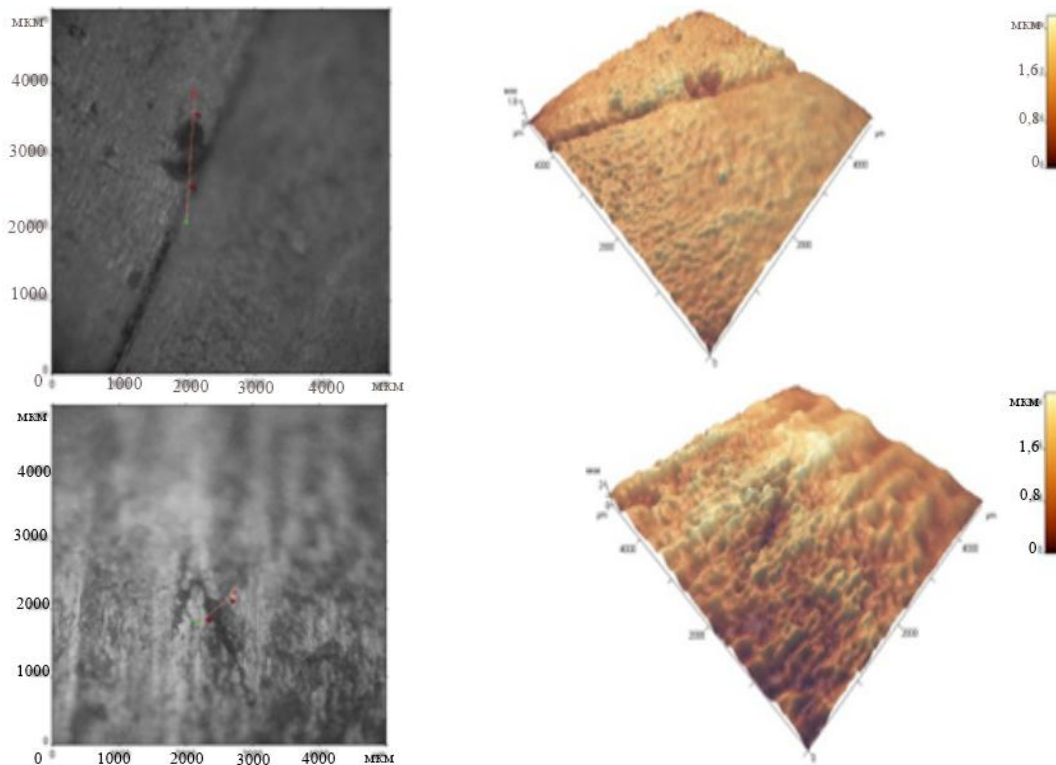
Макрознімок поверхні заготовки № 1 до й після обробки інструментом з кутом деформації 4 градуси після 13 циклів
